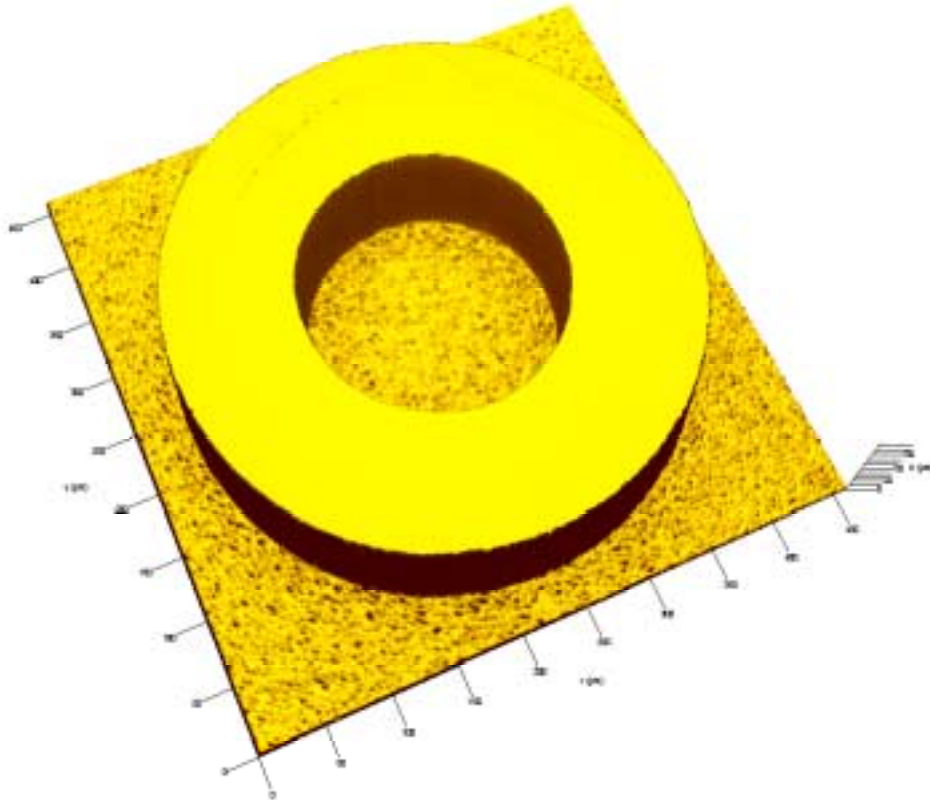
Aufsicht auf eine Ringstruktur, Material PMMA-XT
